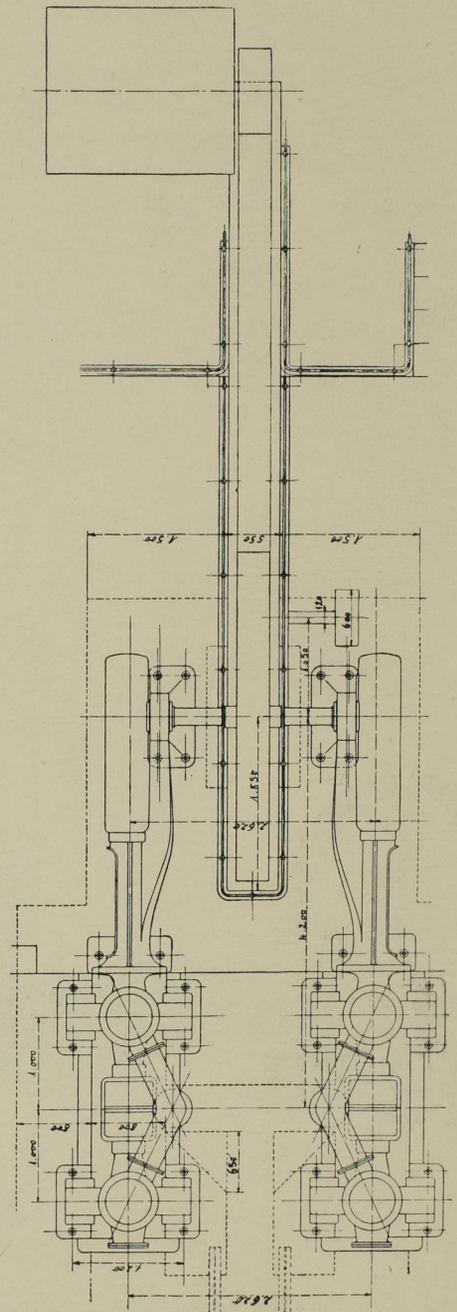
Grundriss der Pumpmaschine. Masst. 1:75.
